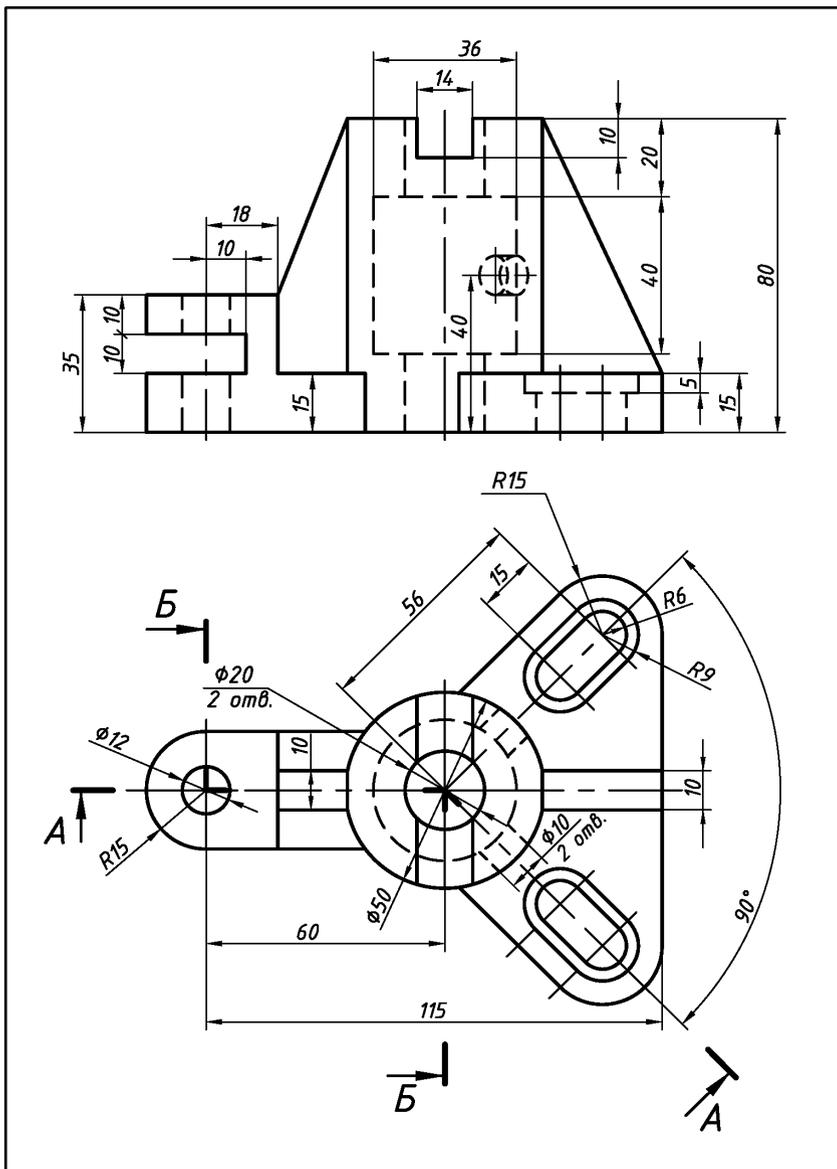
Вариант исходной заготовки чертежа детали для выполнения сложных разрезов
